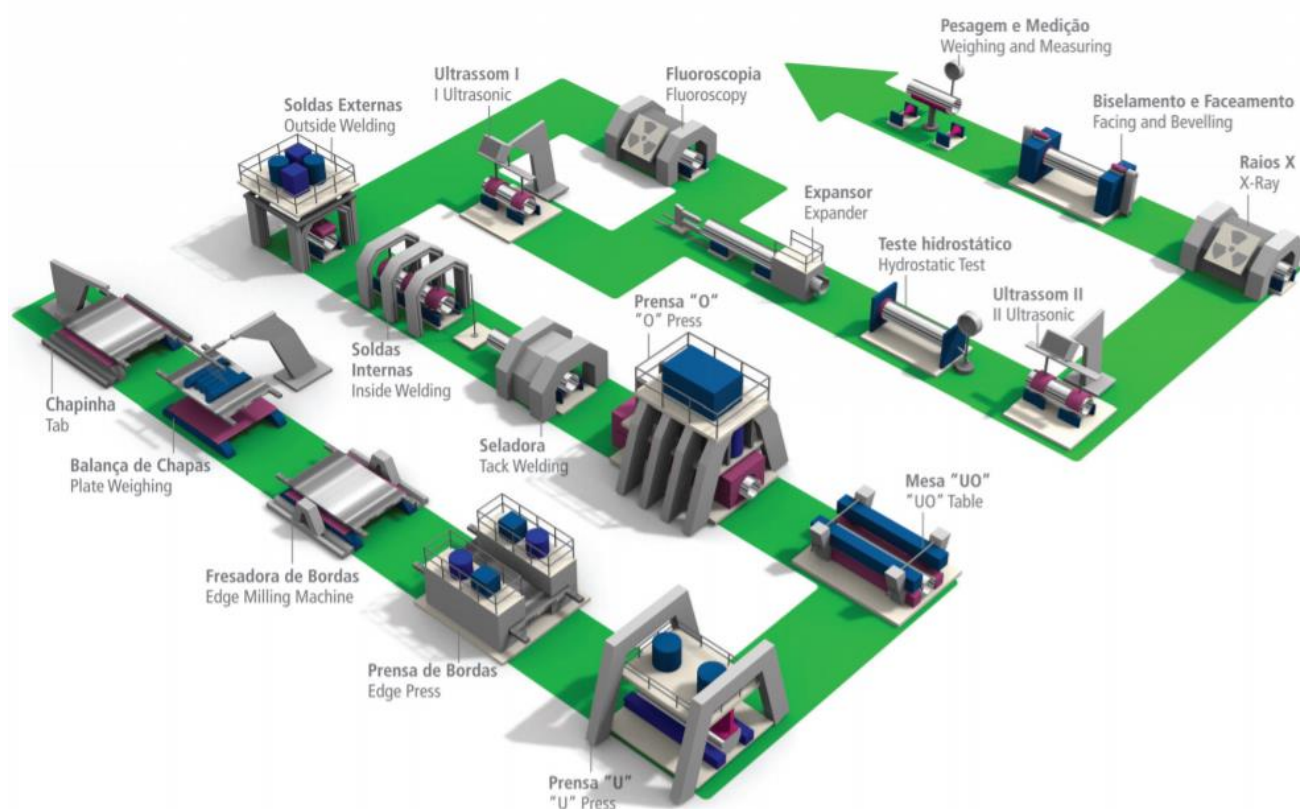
3 - Processo de fabricação de tubos pelo processo de soldagem SAW
